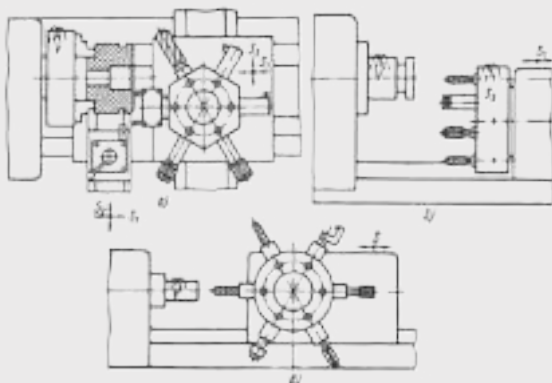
Типи револьверних головок: а — револьверна головка з вертикальною віссю обертання; б — револьверна головка з горизонтальною віссю обертання, яка паралельна з віссю шпинделя; в — револьверна головка з горизонтальною віссю обертання, перпендикулярною до осі шпинделя
